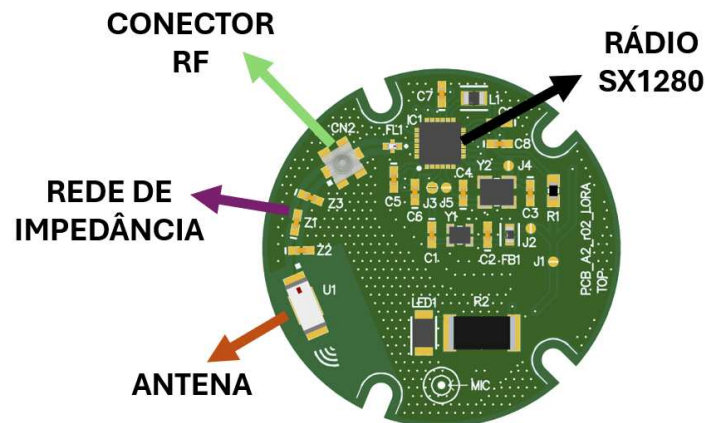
Layout da quarta camada PCB A2 IEEE.
